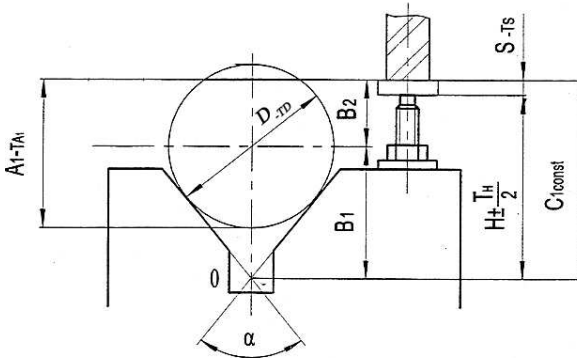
Схема встановлення заготовки на призму та настроювання інструменту при фрезеруванні лиски
